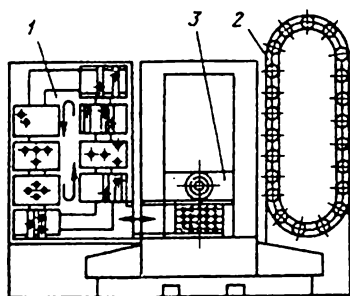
Компоновка багатоцільового верстата з двома магазинами:
